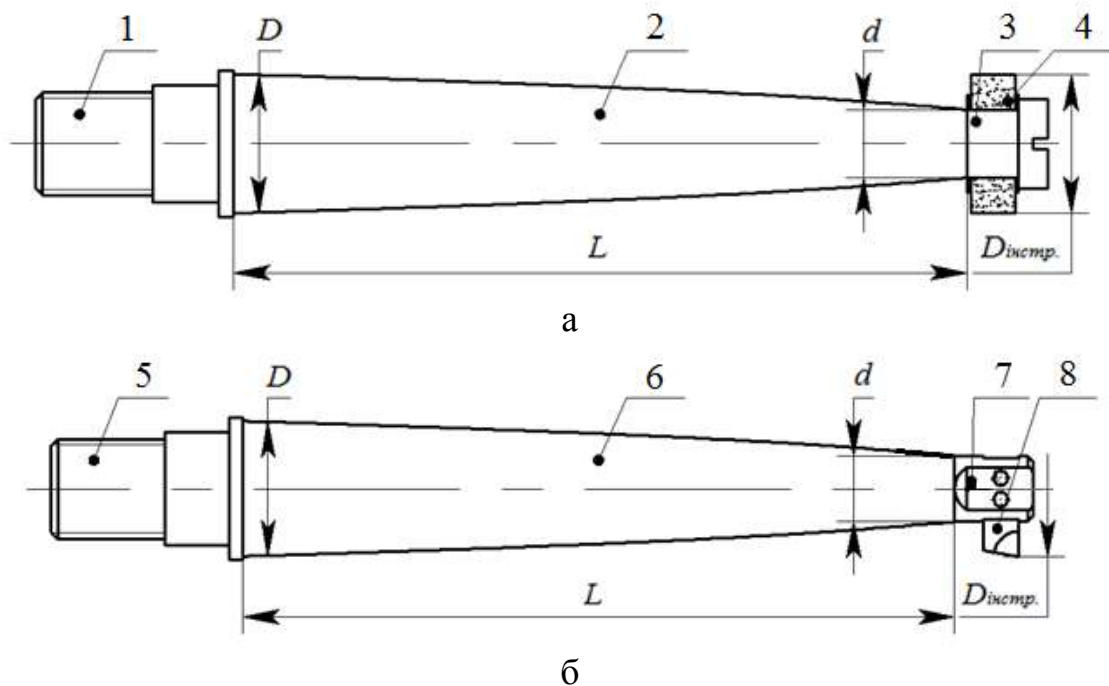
Інструментальні оправки з консольною частиною у формі зрізаного кубічного параболоїда для шліфування (а) та розточування (б)
